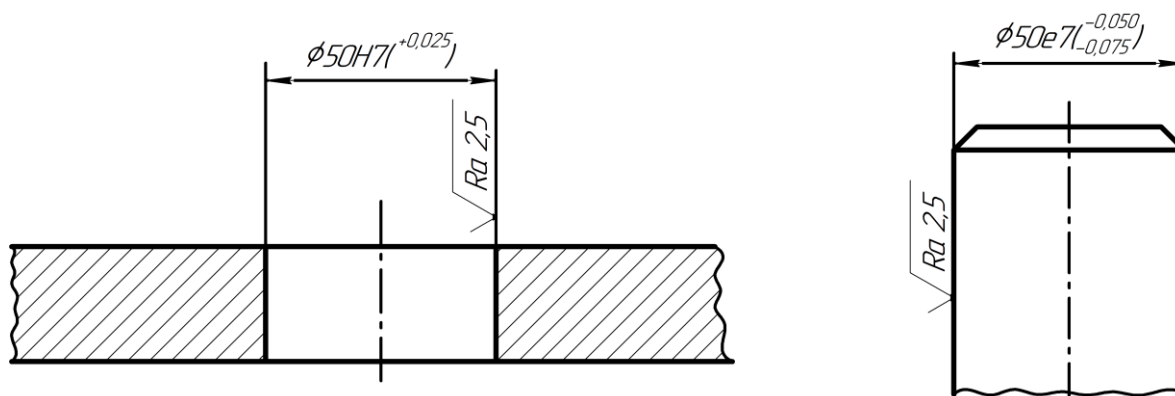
Обозначение допусков размеров на деталировочных чертежах
